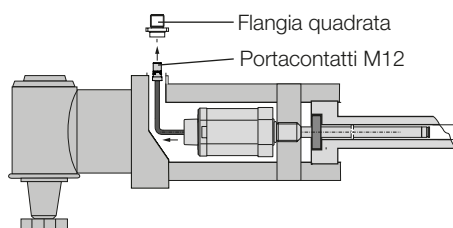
Esempio di sistema ad innesto in un montaggio del trasduttore di posizione in un cilindro idraulico
